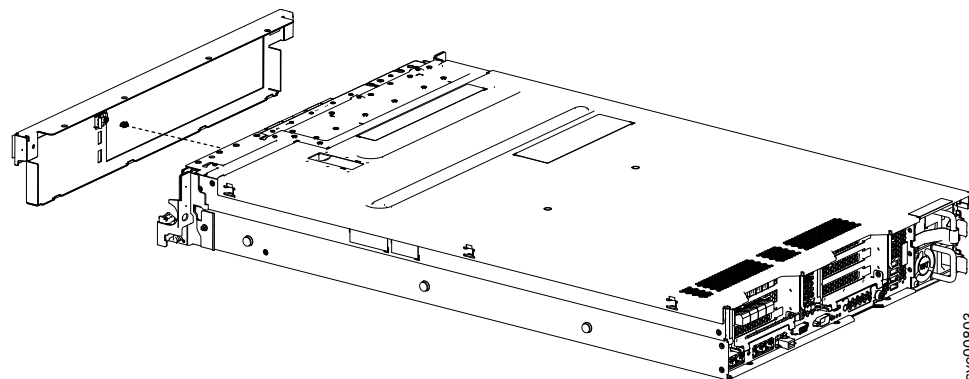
Removendo o cabo do LED para a parte traseira do conjunto de painel
